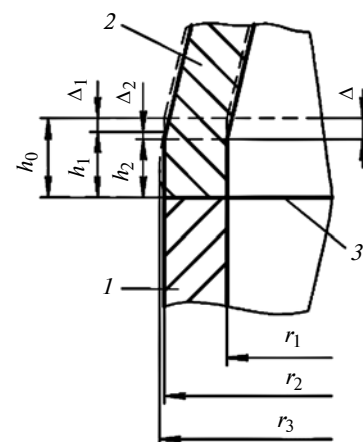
Расчетная схема сварки давлением: 1, 2 — обечайки; 3 — линия сварки
